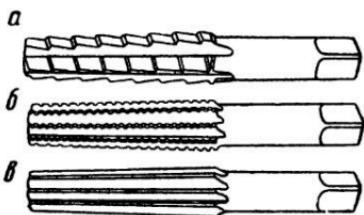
Комплект конических разверток: *а* — черновая; *б* — получистовая; *в* — чистовая.
